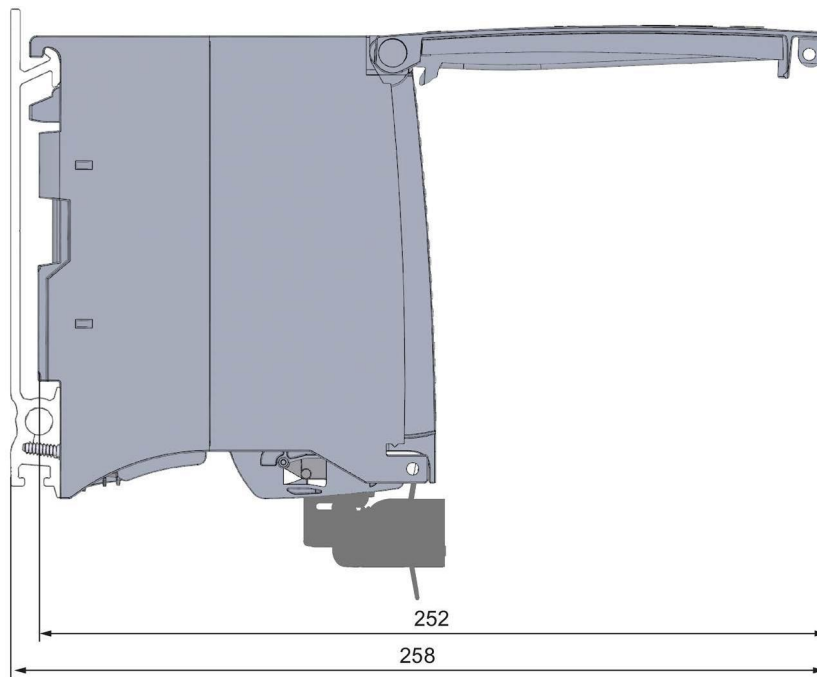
Габаритный чертеж CPU 1512C-1 PN вид сбоку с открытой передней крышкой
